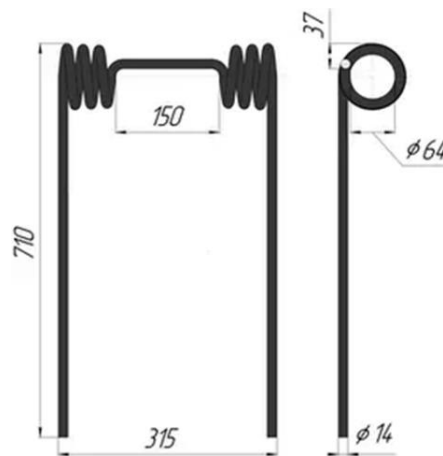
Зуб пружинний із нанесеними розмірами
